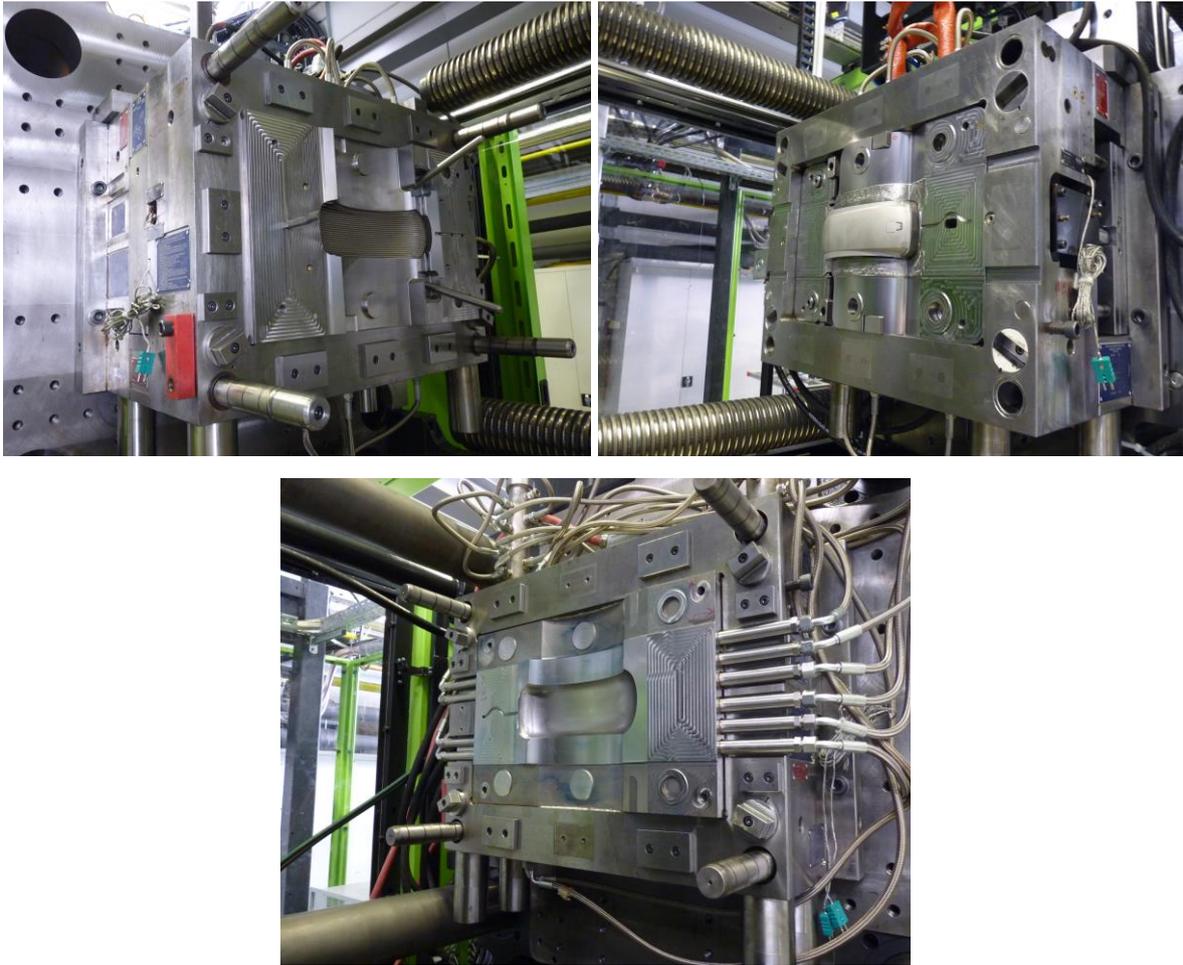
Werkzeug und Demobauteil des 2K-Wendeplattenwerkzeugs Deckel Mittelarmlehne
